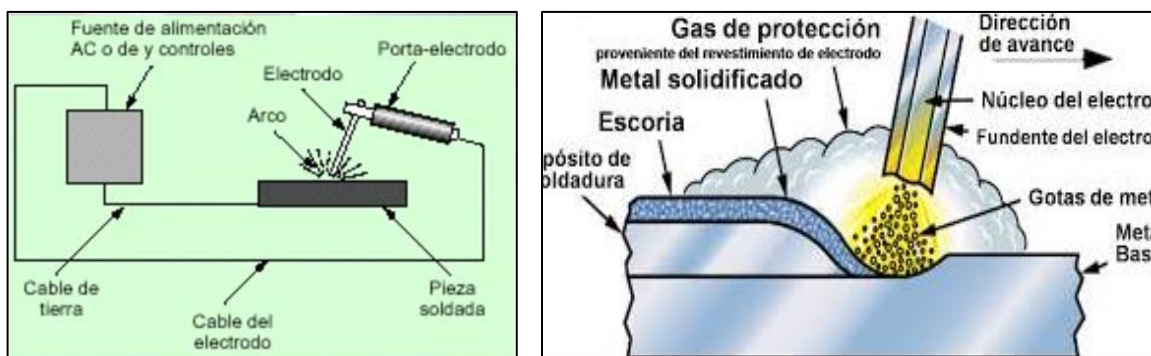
Equipo de soldadura por arco eléctrico y soldadura por arco eléctrico
